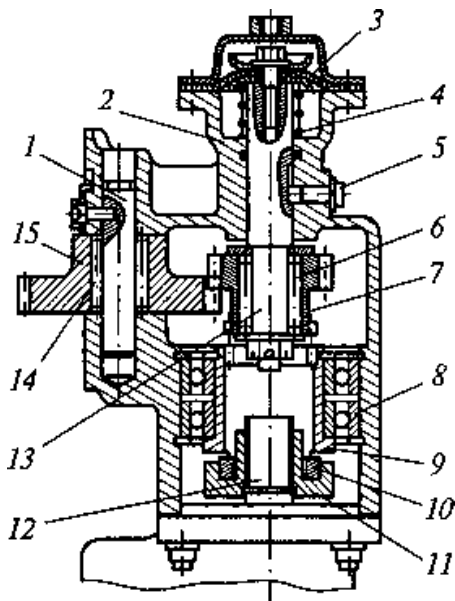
Коробка отбора мощности самосвала КамАЗ-5511
